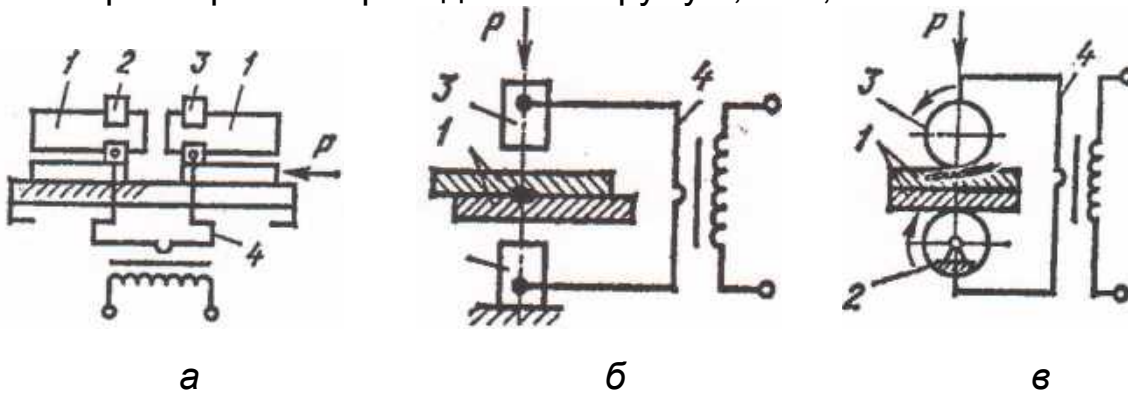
Типові схеми контактеного електричного зварювання:
